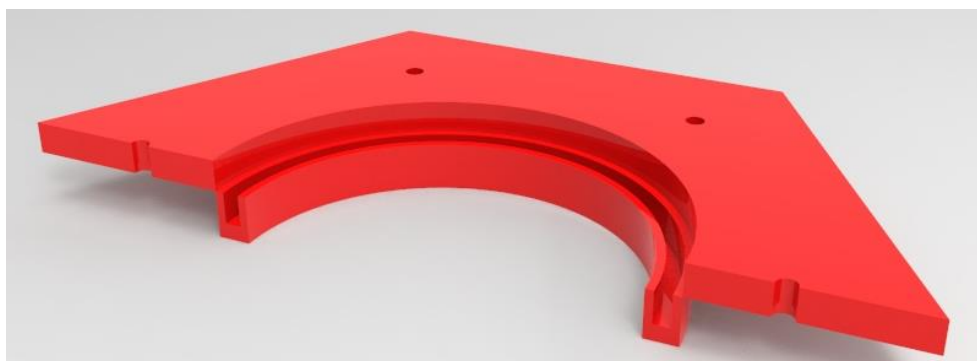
Схема фланца с кольцевой проточкой для отбора конденсата.
